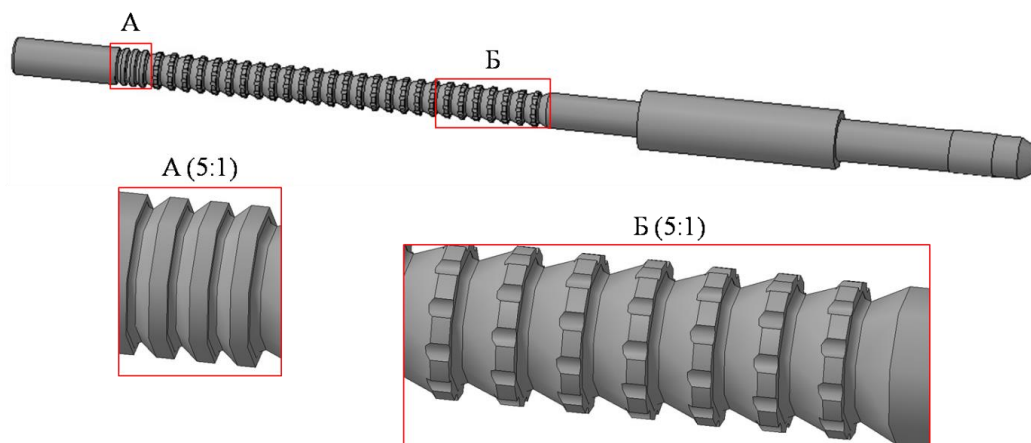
3D модель цилиндрической протяжки. А и Б – выносные элементы режущих и калибрующих зубьев протяжки соответственно.
